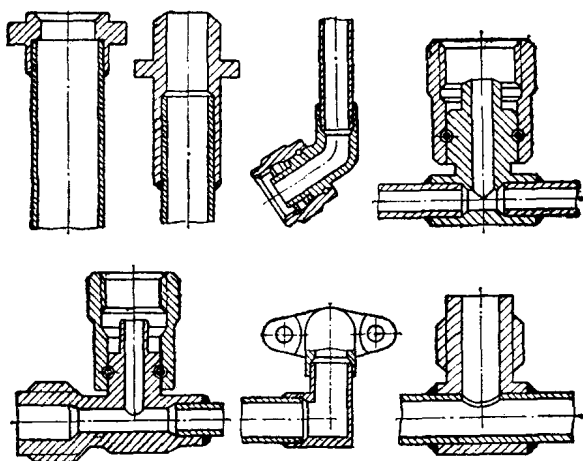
配件与管子的典型焊接和钎接的接头形式
